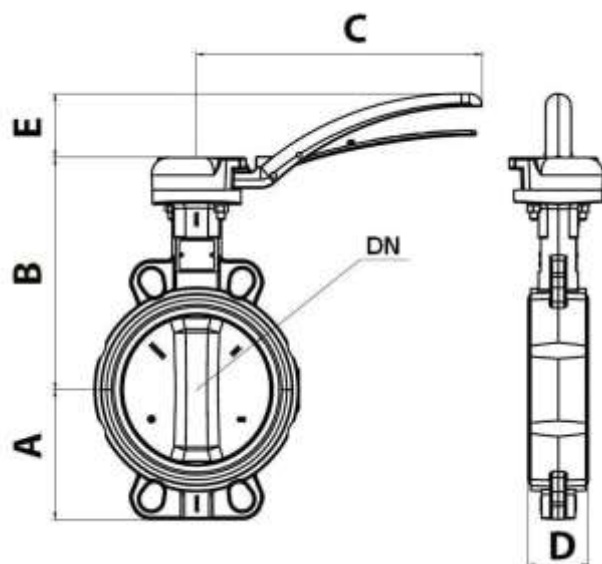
Габаритные и присоединительные размеры затворов дисковых поворотных модификации VFY- WH с центрирующими проушинами
